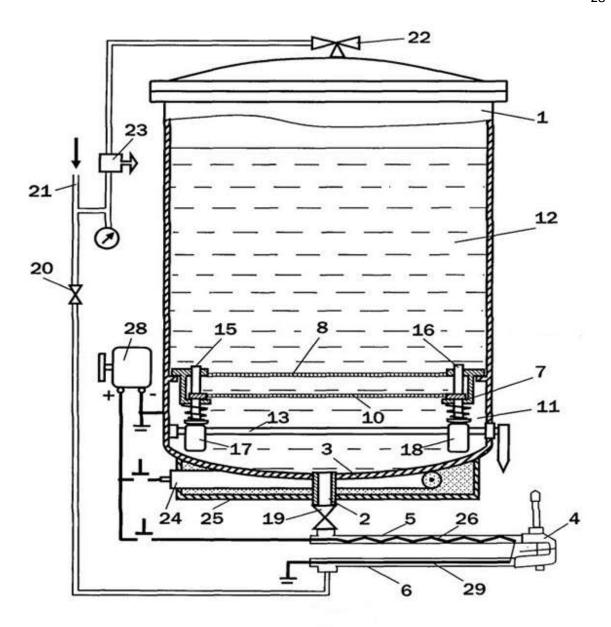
Патент РФ № 2460590 устройство для нагрева защитной смазки при нанесении.
